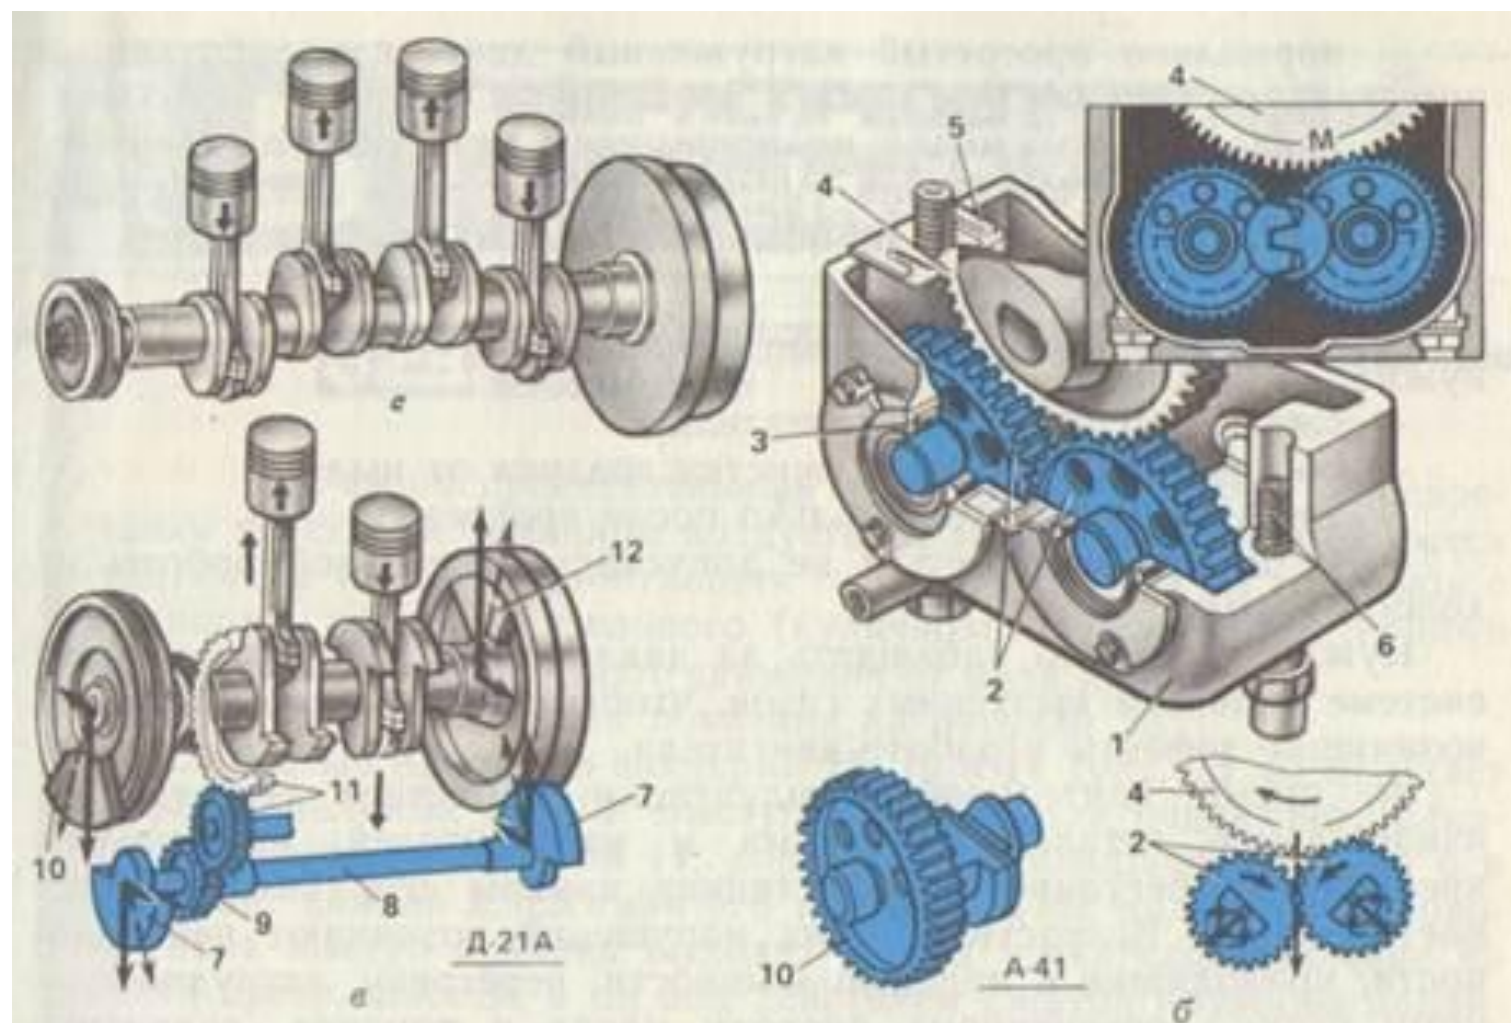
Схемы уравнивания дизелей и детали уравнивающего механизма: а — схема уравнивания четырехцилиндровых дизелей Д-240 и Д-144; б — уравнивающий механизм дизеля А-41; в — схема уравнивающего механизма двухцилиндрового дизеля Д-21А; 1 — корпус уравнивающего механизма; 2 — шестерни-грузы; 3 — роликовый подшипник; 4 — зубчатый венец шейки коленчатого вала; 5 — регулировочные прокладки; 6 — болт крепления корпуса; 7 — груз; 8 — вал уравнивающего механизма; 9 — шестерня вала; 10 — прилив на шкиве; 11 — промежуточные шестерни; 12 — прилив на маховике.
